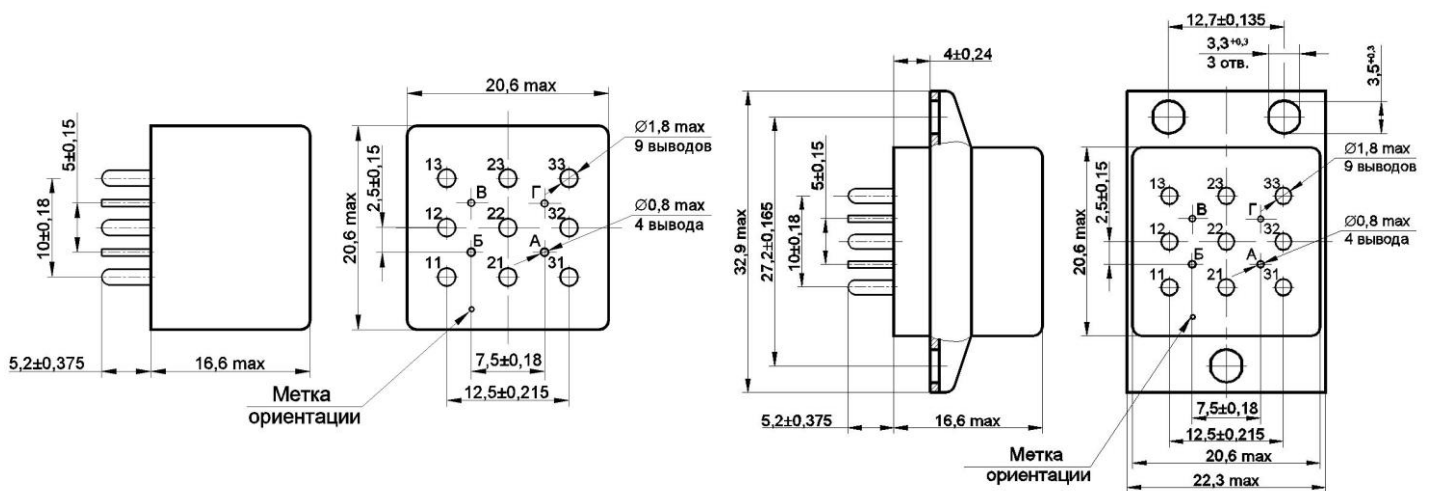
Общий вид реле исполнений РВИМ.647614.075, -01, -04, -05, -08, -10 без фланца с габаритными и присоединительными размерами
